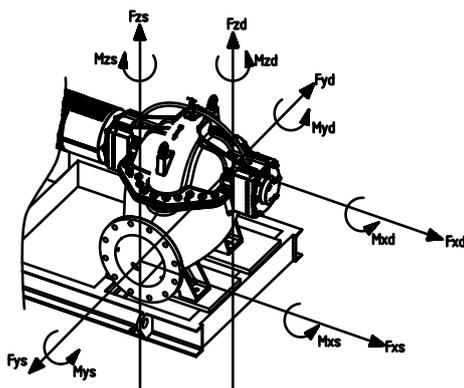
Forze e coppie ammesse per le flange della pompa – pompa in ghisa grigia
